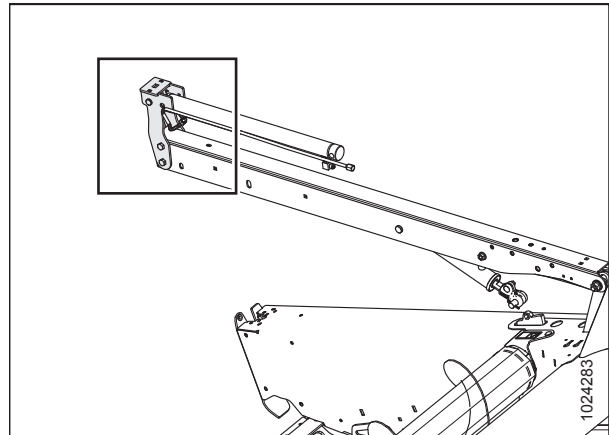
Bras droit – similaire aux bras central et gauche (parties cachées pour plus de clarté)
